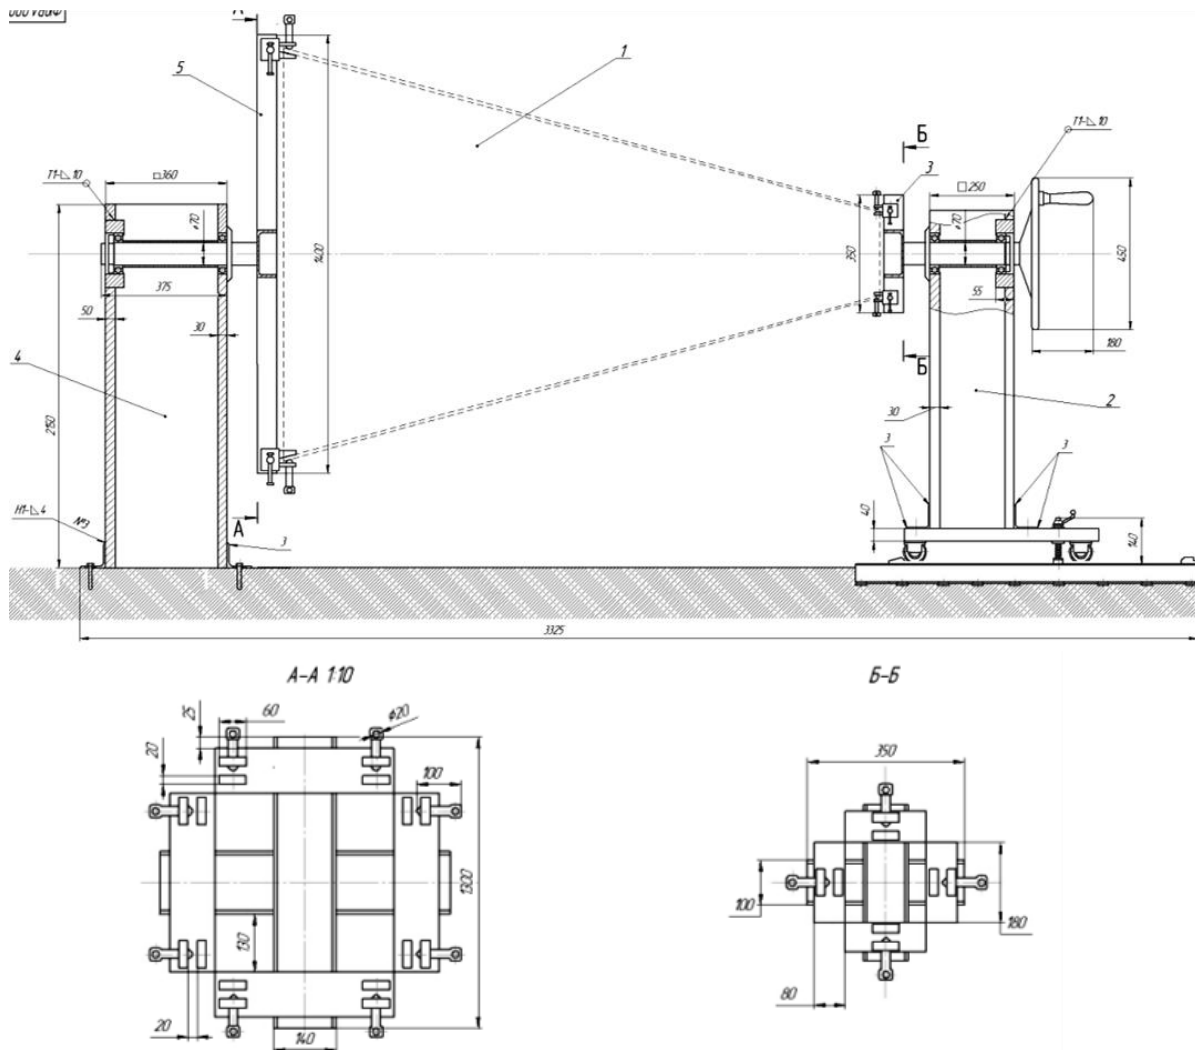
Приспособление для сборки и сварки бункера
